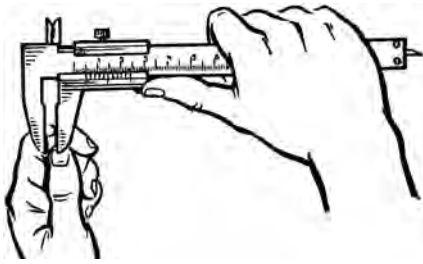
Положення рук щодо патрона штангенциркуля і незакріпленої деталі
